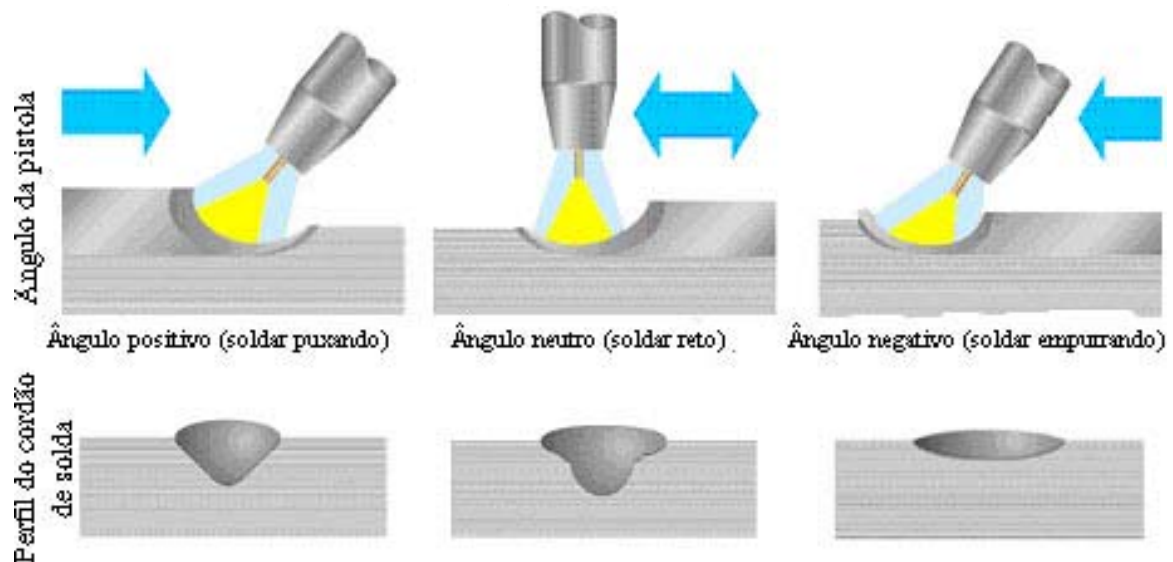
Ângulos de soldagem (Fortes, 2004)
